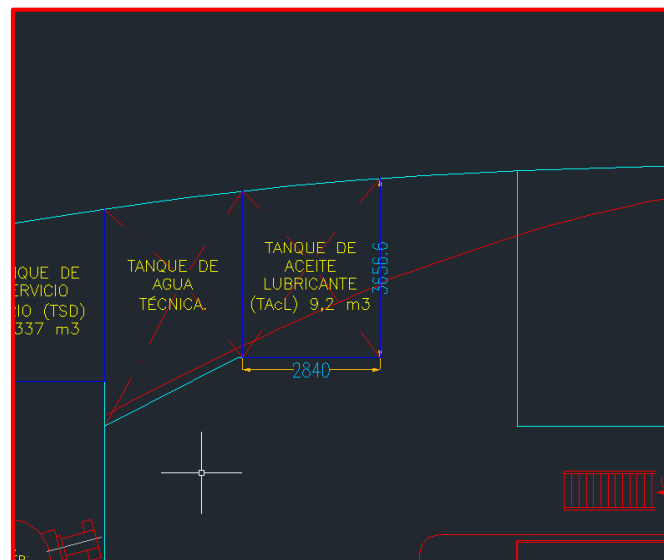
Tanque de aceite lubricante / vista superior (planta)
